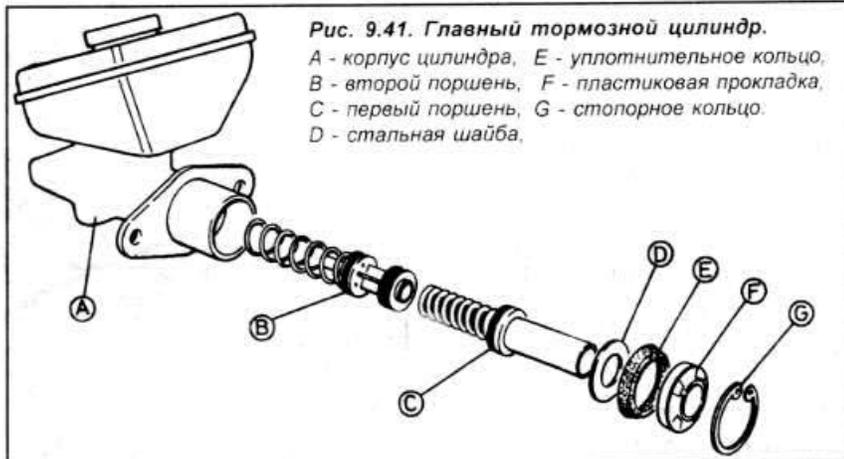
Главный тормозной цилиндр. А - корпус цилиндра, Е - уплотнительное кольцо, В - второй поршень, F - пластиковая прокладка, С - первый поршень, G - стопорное кольцо. D - стальная шайба.
